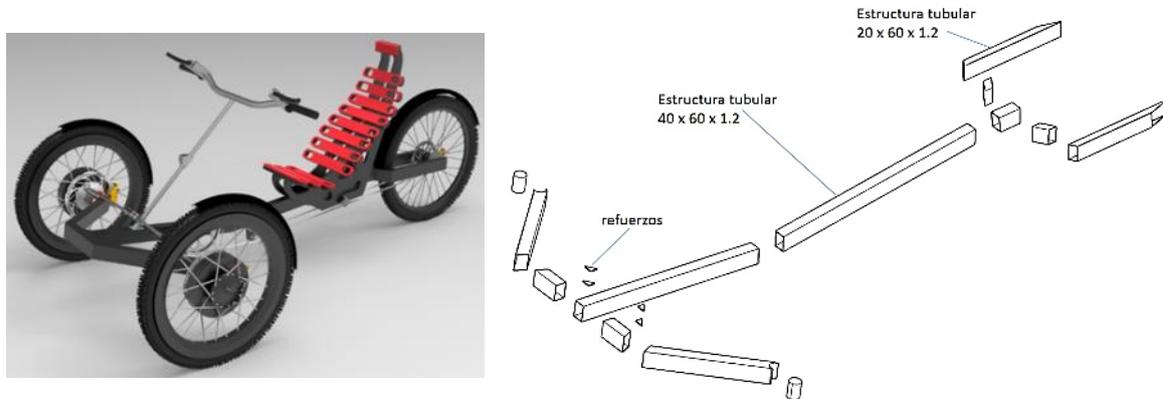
Izquierda: perspectiva del chasis y el asiento. Derecha: Despiece de la estructura del chasis.
